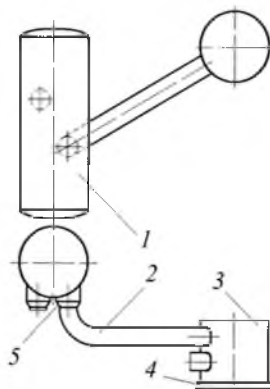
Схема “горячей” ветви первого контура реактора (вид сверху и сбоку): 1 – парогенератор (ПГ); 2 – главный циркуляционный трубопровод (ГЦТ); 3 – корпус реактора; 4 – опорный бурт корпуса реактора; 5 – узел приварки.
